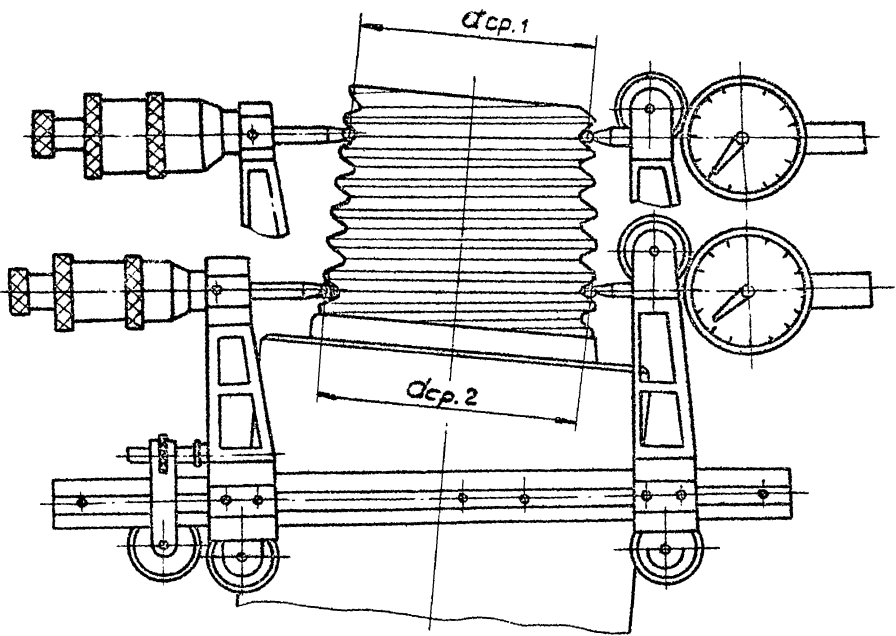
Проверка конусности наружной резьбы накладным прибором типа "ИНК".
